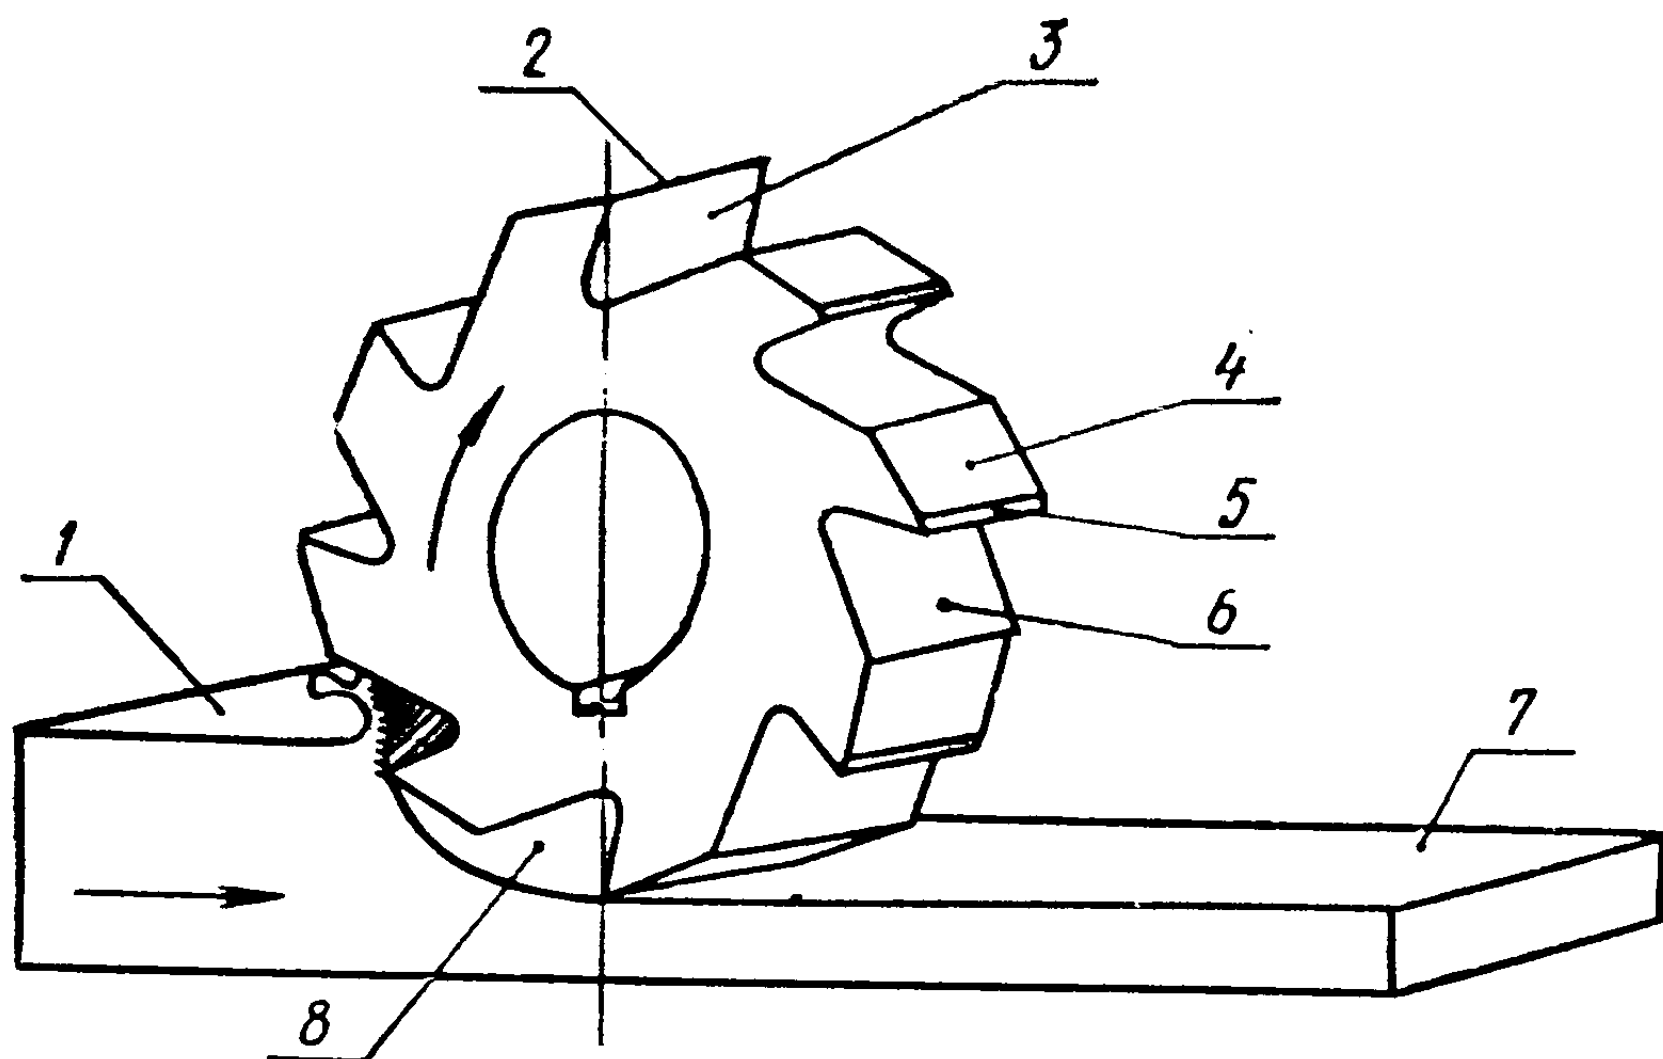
Элементы цилиндрической фрезы и поверхности обработки.
